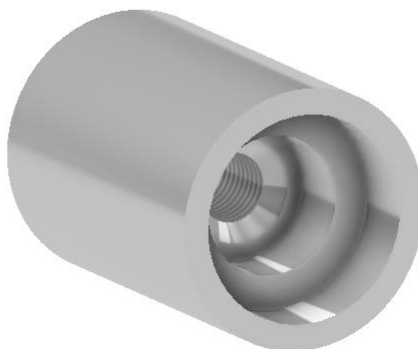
Τρισδιάστατη απεικόνιση αποστολής 58
